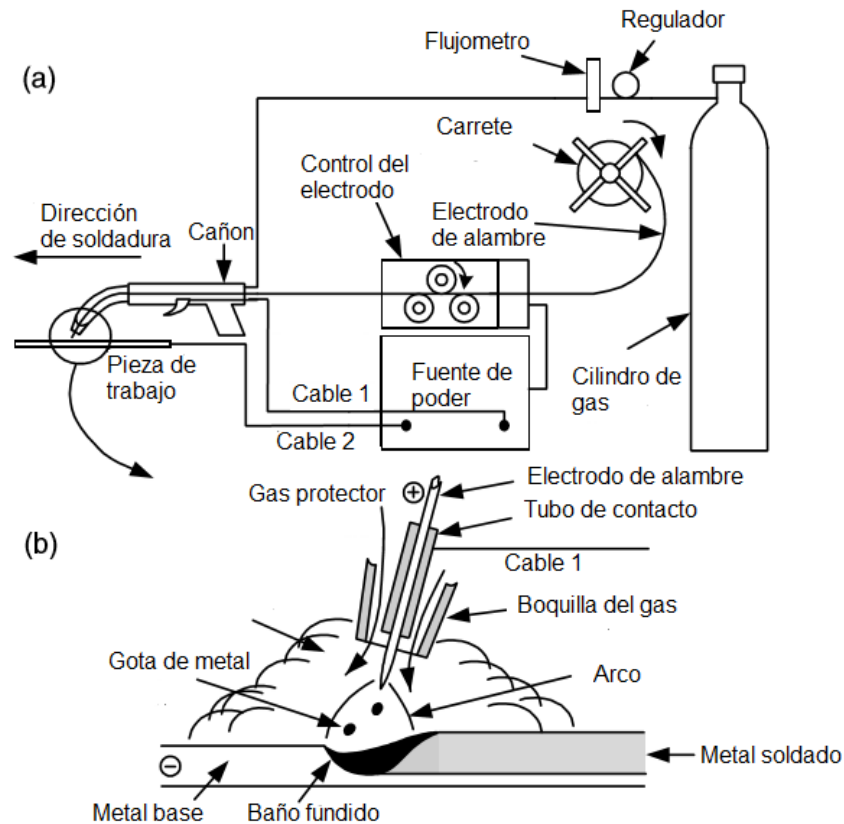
Esquema general del proceso de soldadura GMAW (a) y esquema del área donde se efectúa la soldadura (23).
